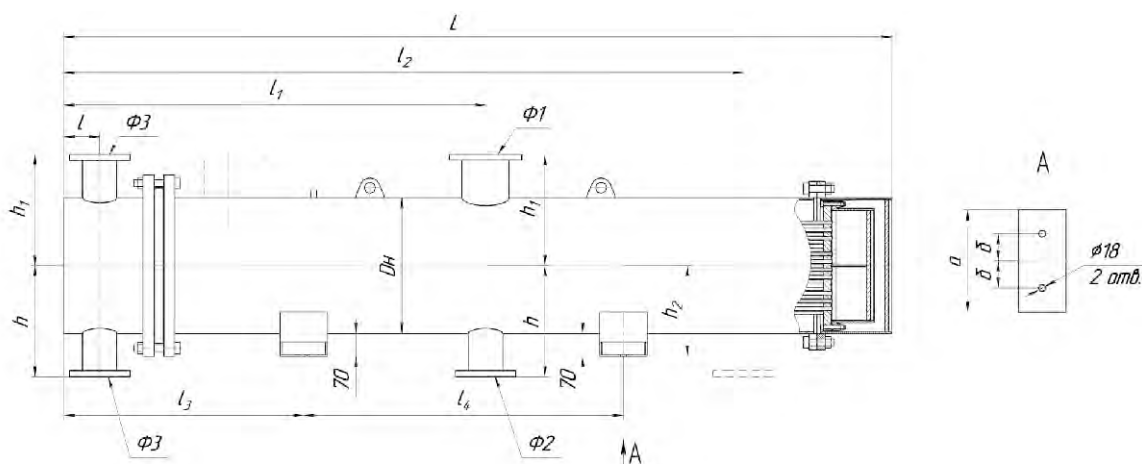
Габаритные и присоединительные размеры подогревателей МВН.
